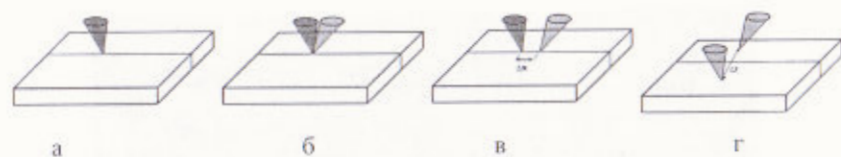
Различные способы лазерной сварки. а – однолучевая сварка; б – двухлучевая суперпозиционная сварка; в – двухлучевая последовательная сварка; г – параллельная сварка
